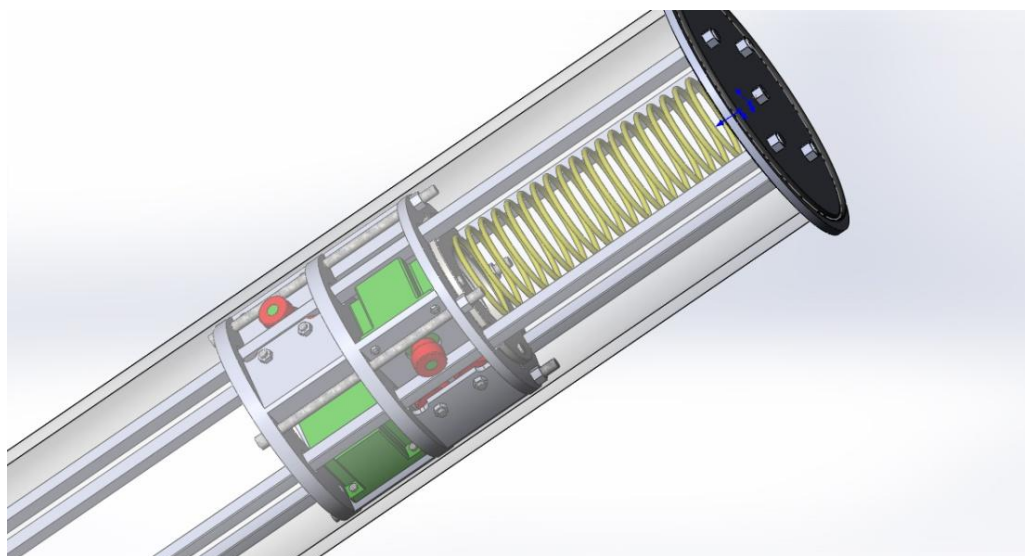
Вид расположения элементов конструкции блока Вл мЭС
